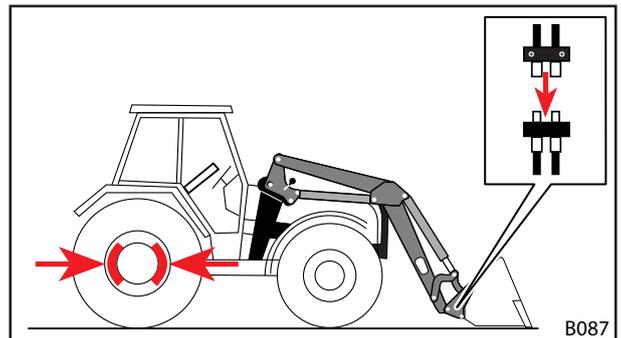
Collegare le tubature idrauliche dell'attrezzo con attacchi del caricatore frontale
